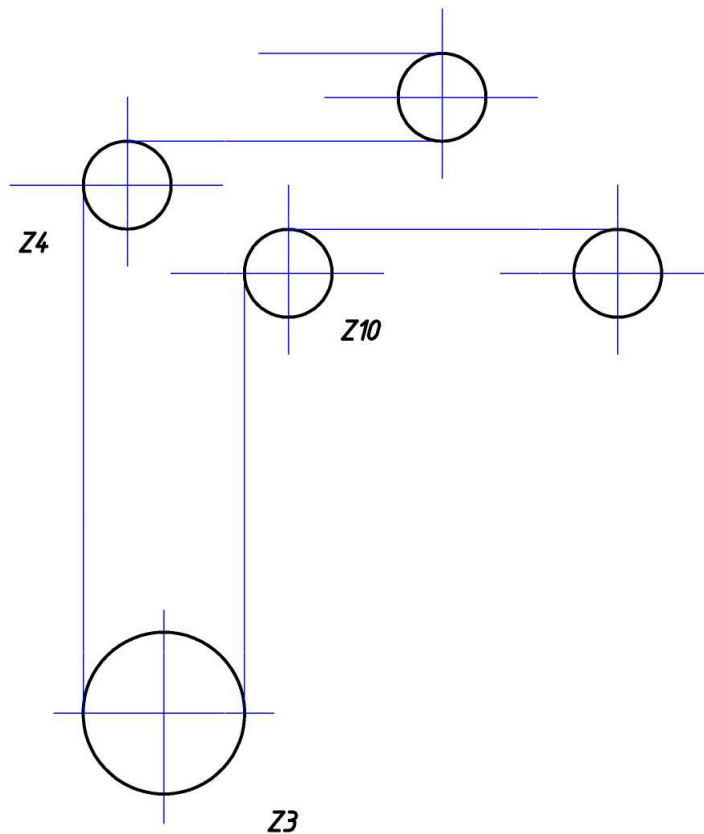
Фрагмент ланцюга конвеєру розстійної шафи агрегату кінцевого розстоювання марки Т1-ХР-2А-30
